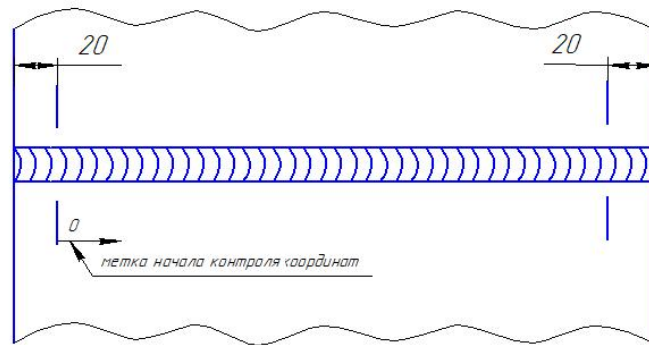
Эскиз сварного соединения и образца
